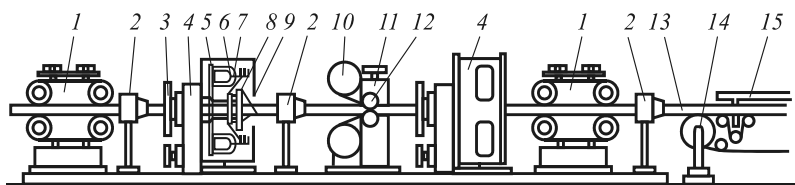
Агрегат для сборки рукавов навивочной конструкции дорновым способом:
